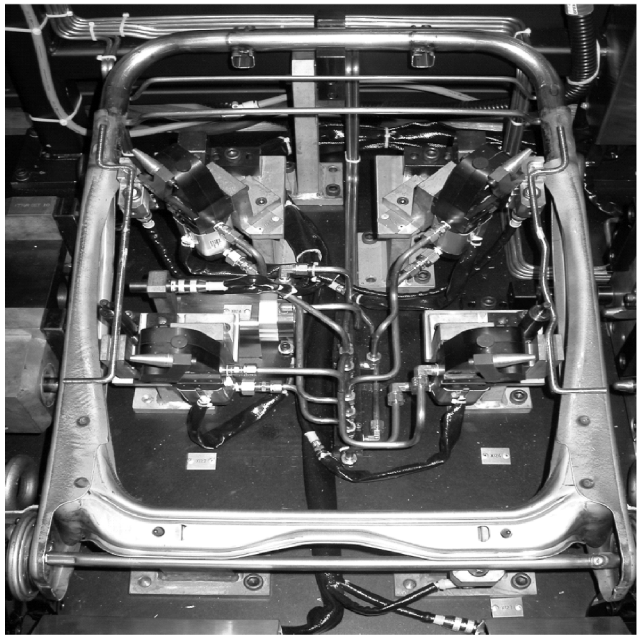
汽车白车身零部件四焊点点焊装夹具
